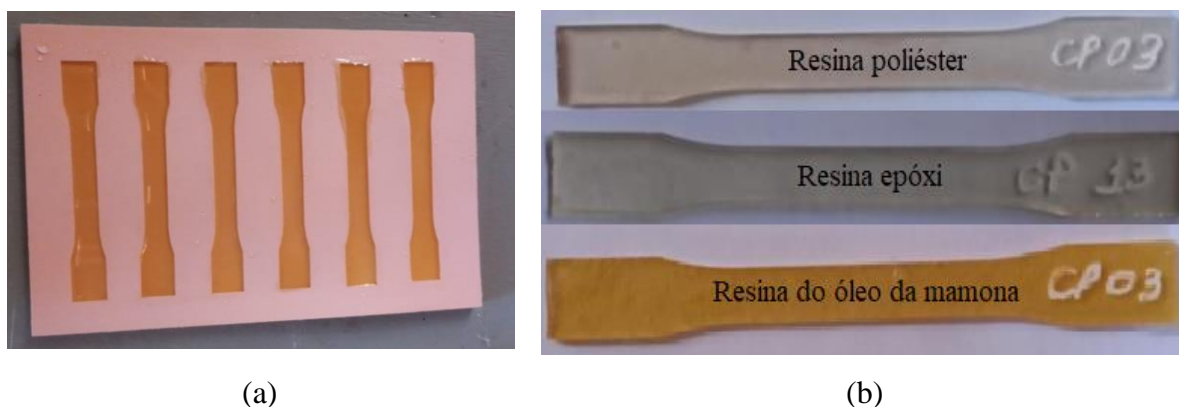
Resinas: (a) processo de moldagem; (b) corpos de prova para ensaio de tração.
